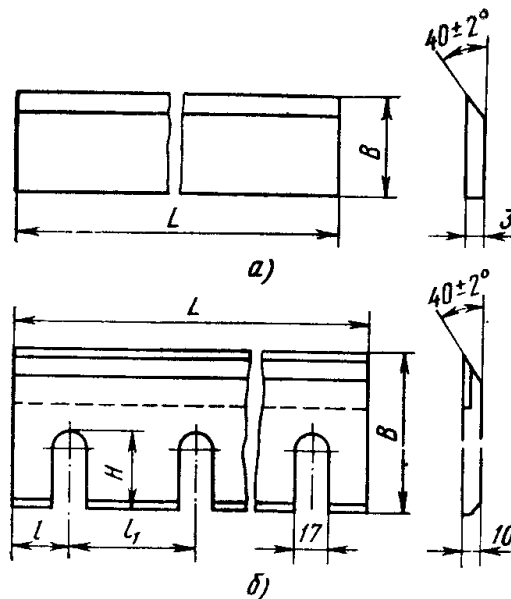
Ножі для плоского фрезерування деревини без прорізів (а) і з прорізами (б).
